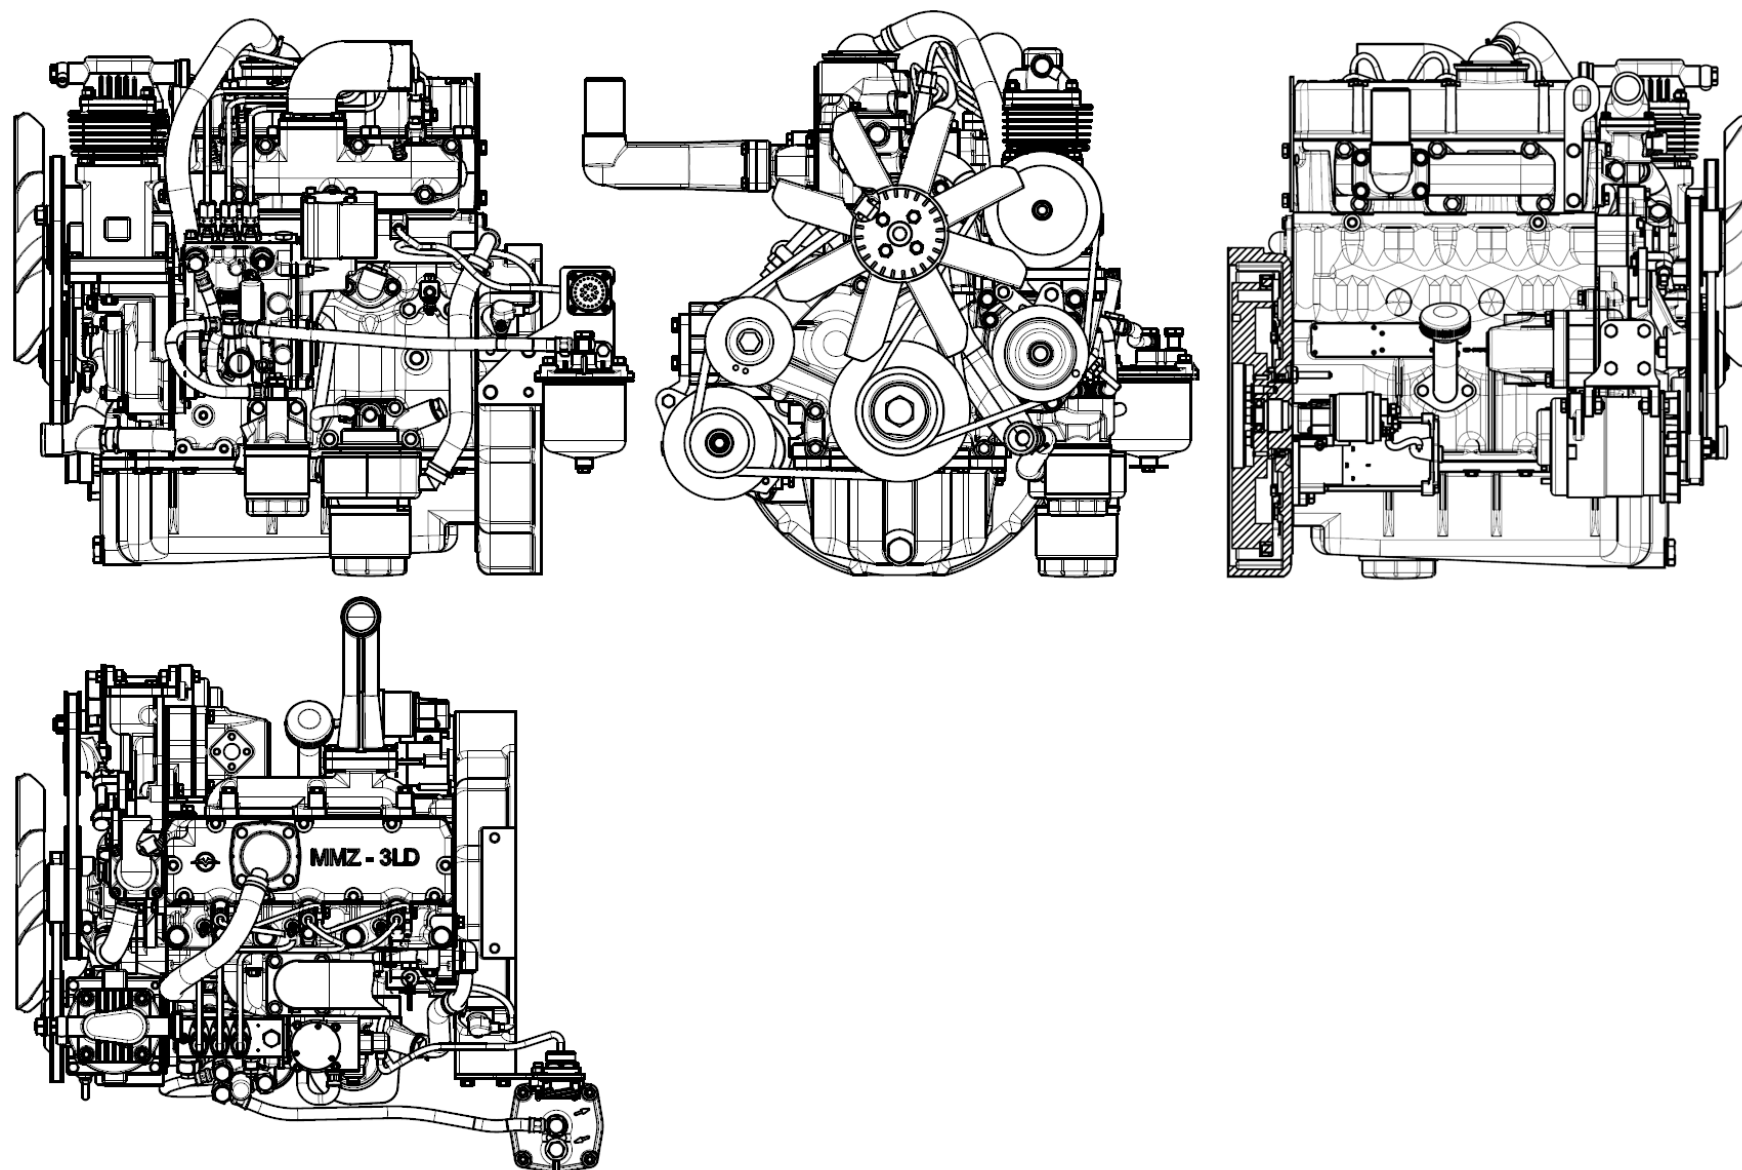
а – Общий вид дизеля MM3-3LD-00
